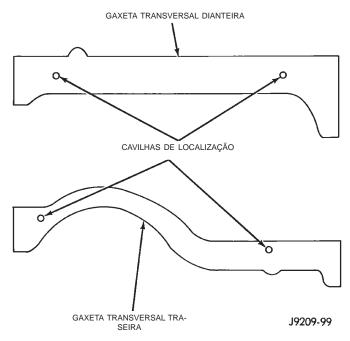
Gaxetas Transversais e Cavilhas de Localização
